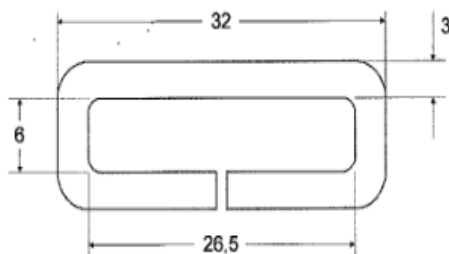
Vista da argola retangular do tirante inferior (medidas em mm)
